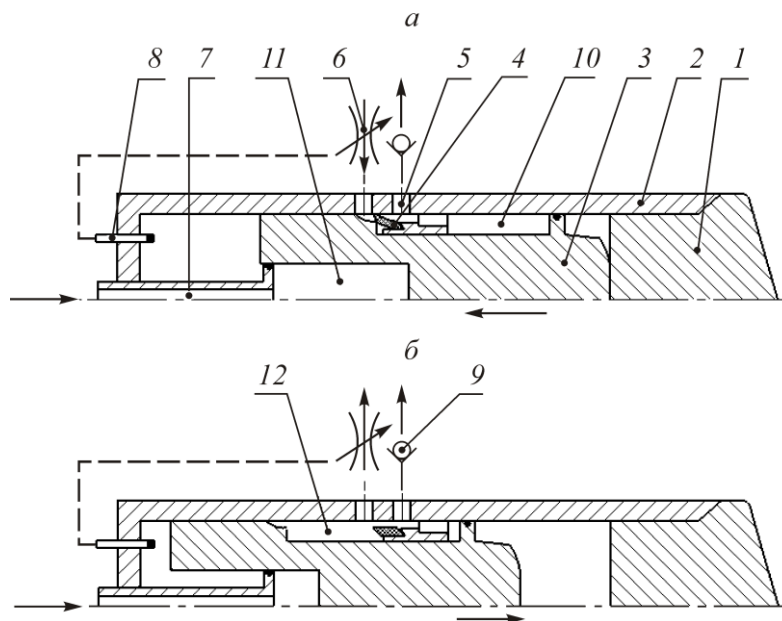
Конструктивная схема гидроударного устройства с промежуточной камерой: 1 — накопитель; 2 — корпус; 3 — ударник; 4 — упругий клапан; 5 — сливное отверстие; 6 — золотник распределителя; 7 — канал подвода сжатого воздуха; 8 — датчик; 9 — обратный клапан; 10 — промежуточная камера ударника; 11 — камера рабочего хода ударника; 12 — камера холостого хода ударника
